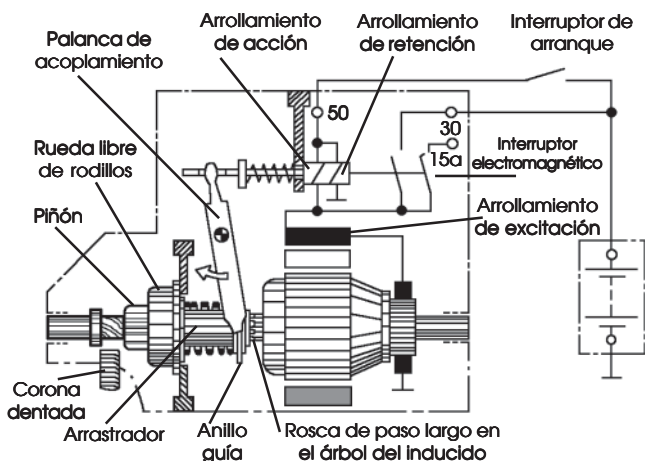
Arrancador de piñón corredizo con movimiento rotatorio de engrane
